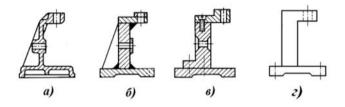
Варианты изготовления корпуса приспособления: a — литого; b — сборного; r - кованного.
